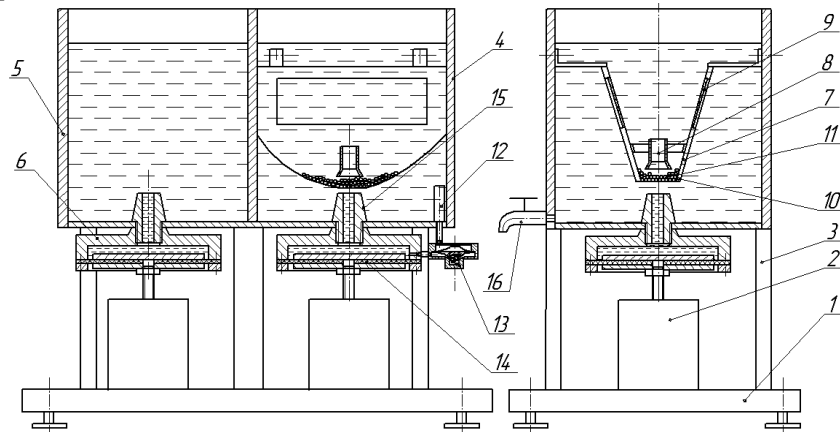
Загальний вигляд конструкції вібраційної машини для очистки та мийки деталей: 1- основа; 2 – вібраційний привод ексцентрикового типу; 3 – стойки; 4 – ванна очистки; 5 – ванна мийки; 6 - гідропульсатор; 7 – короб; 8 – сопло; 9 – сітка; 10 – сітка; 11 – кульки з полістиролу; 12 – трубка; 13 – мембранний клапан; 14 – гумова мембрана з дисками; 15 – сопло; 16 – кран зливний
